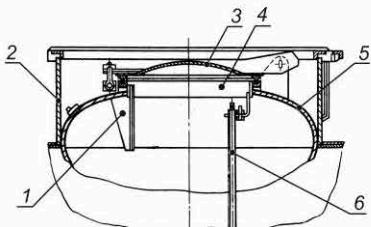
Расширительный колпак цистерны для виноматериалов:
